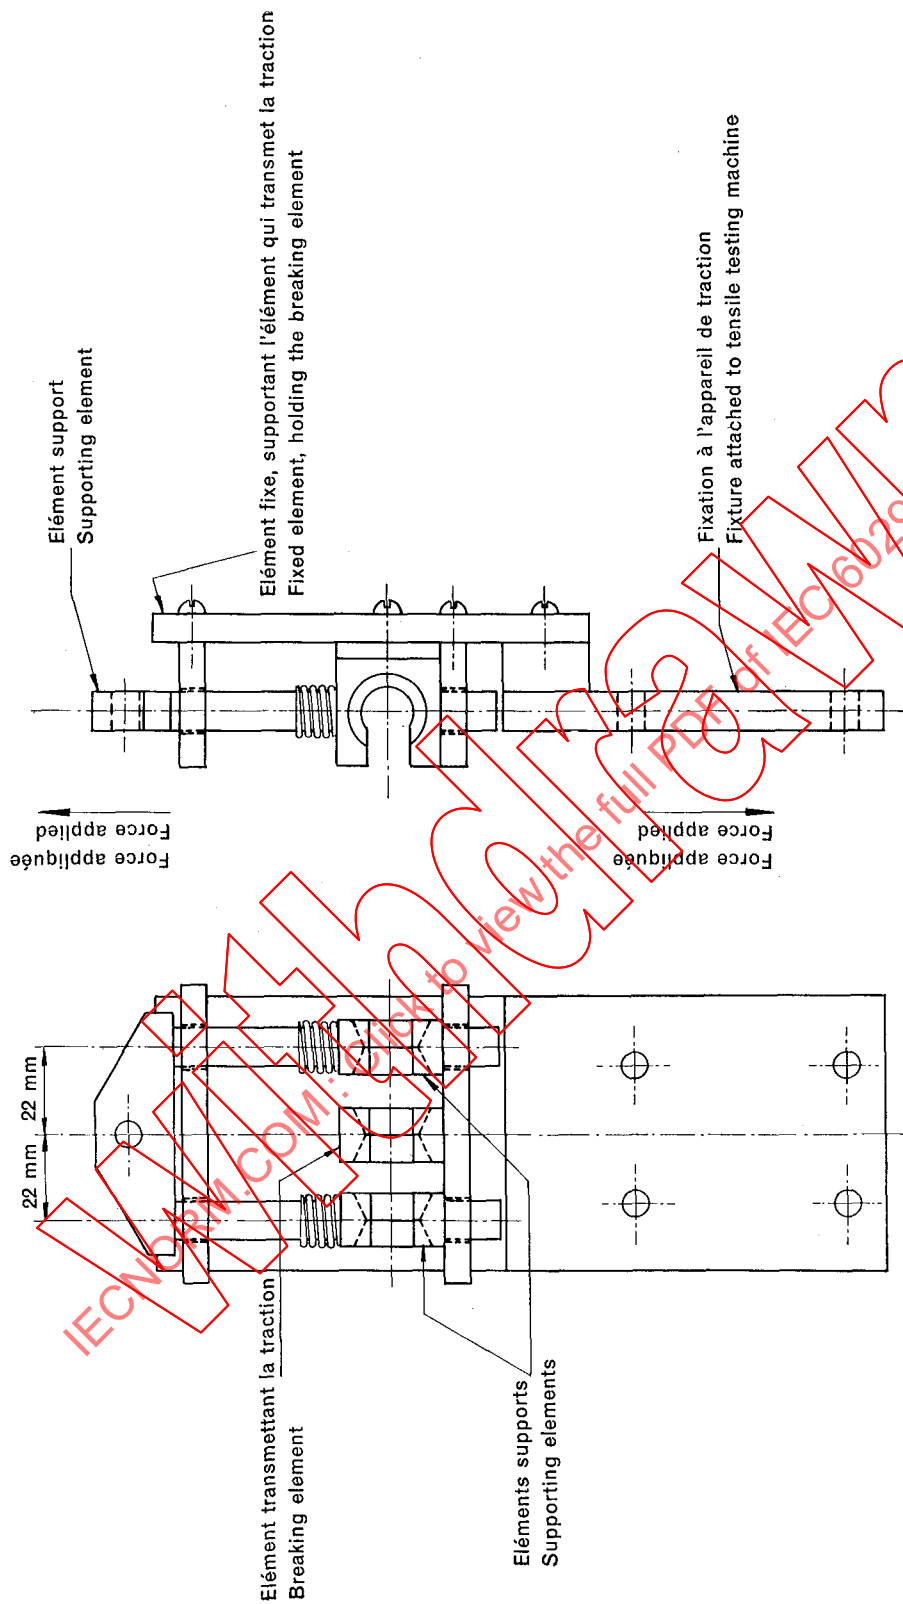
Exemple de montage de fixation pour l'essai d'adhérence du vernis.
